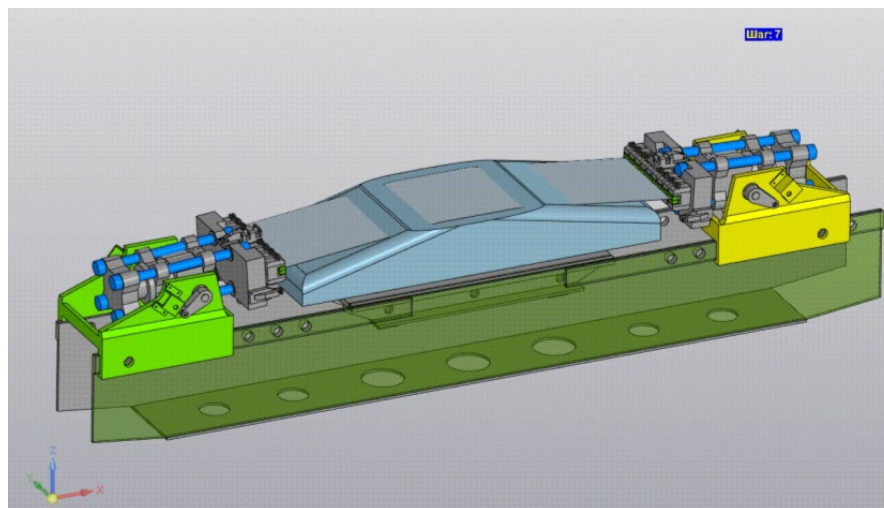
Пример виртуальной станки РО-3М для обтяжки листовой заготовки
